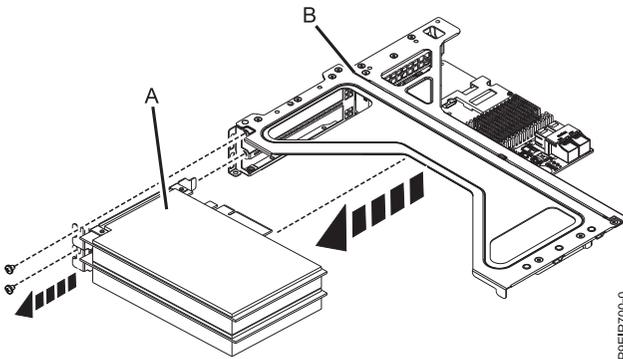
Removendo um adaptador PCIe da posição 2 ou 3 do riser
